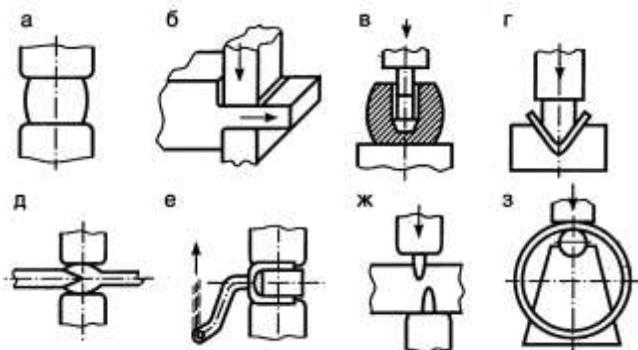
Схема основных операций машиннойковки: а – осадка; в – протяжка; в – прошивка; г – гибка; д – сварка; е – скручивание; ж – отрубка; з – раскатка
